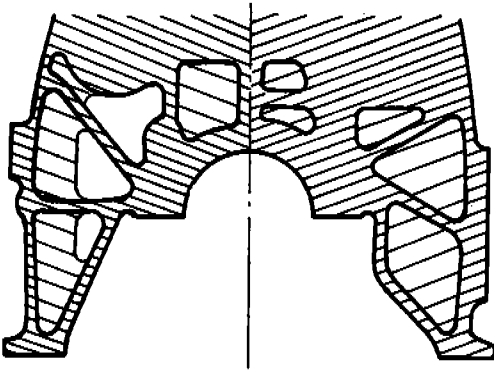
Cylinder block의 Bulk Head Rib 형상 개선
